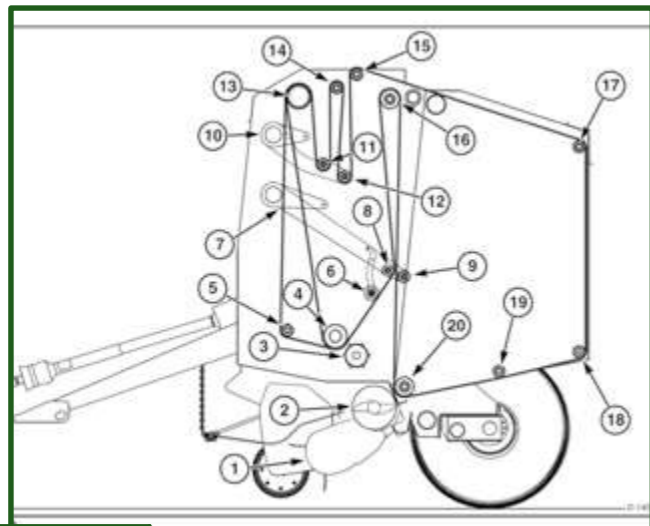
Esquema rotoenfardadora de cámara variable tipo garganta vertical abierta. Vista lateral izquierda: (1) Conjunto del cabezal pickup (2) Sinfín y acelerador de forraje (3) Rodillo de inicio (4) Rodillo de mando inferior (5) Rodillo escalonado (6) Conjunto de rueda formadora del rollo (7) Brazo de densidad del rollo (8) Rodillo frontal de densidad del rollo (9) Rodillo trasero de densidad del rollo (10) Brazo de tensión de correa (11) Rodillo frontal de tensión de correa (12) Rodillo trasero de tensión de correa (13) Rodillo de mando superior (14) Rodillo intermediario frontal superior (15) Rodillo intermediario trasero superior (16) Rodillo superior de la cámara (17) Rodillo superior trasero de compuerta trasera (18) Rodillo inferior trasero de compuerta trasera (19) Rodillo intermediario inferior de compuerta trasera (20) Rodillo intermediario inferior delantero de compuerta trasera.
